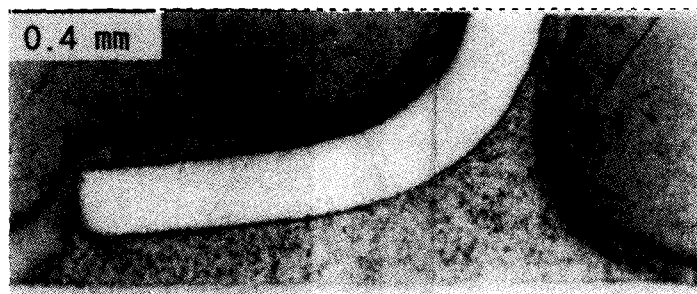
솔더링(soldering) 접합 부위의 단면(2.9W, 700ms, Sn-37Pb solder)
